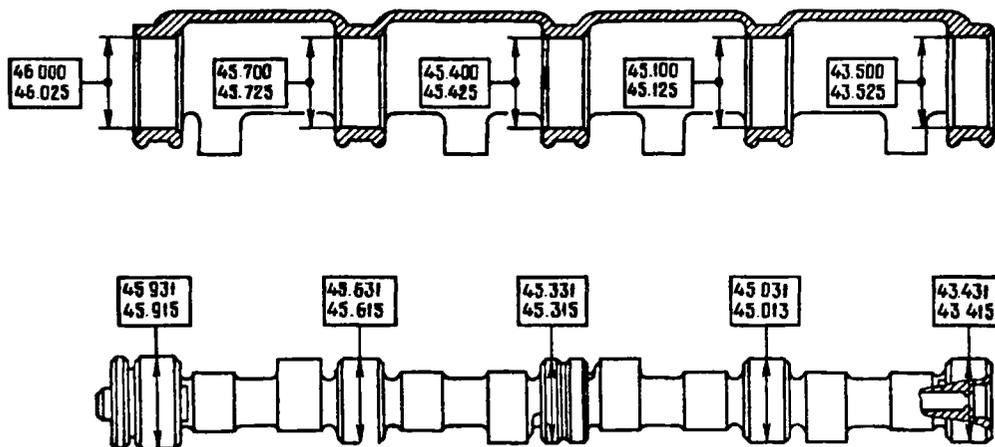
Основные размеры распределительного вала и расточек в корпусе подшипников распределительного вала
